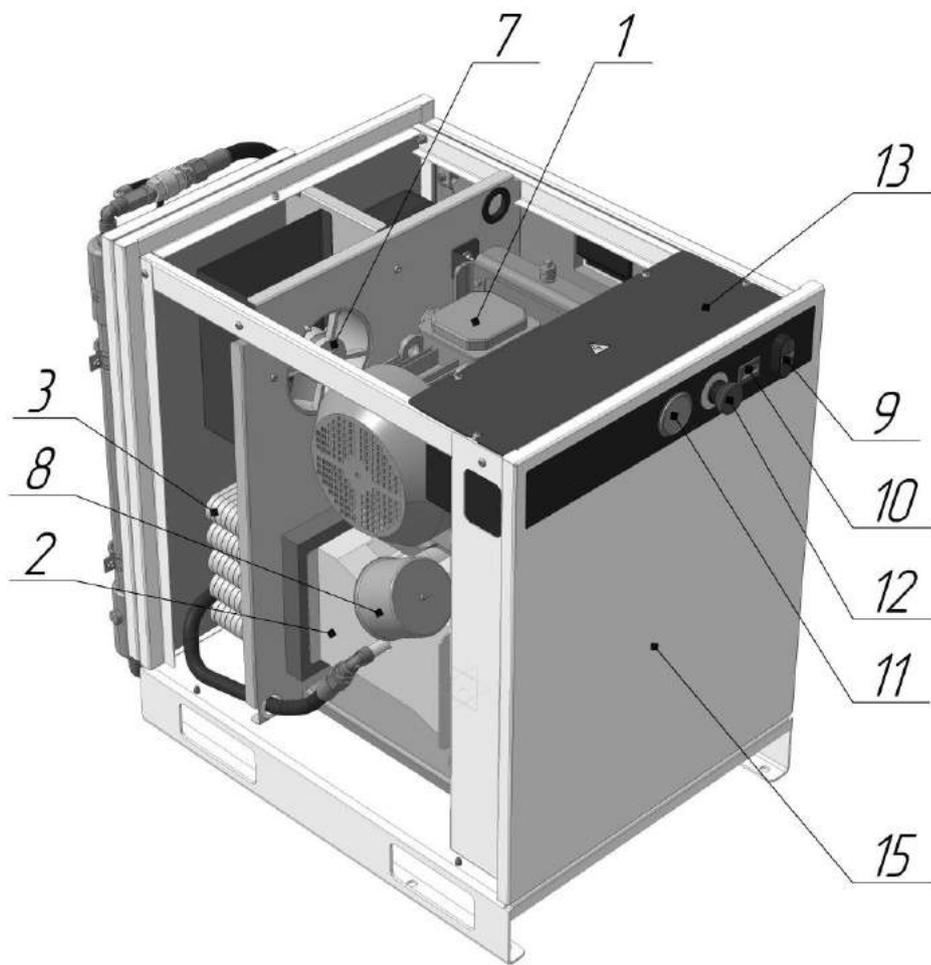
Общий вид компрессорных установок КС3-...М, КС5-...М
